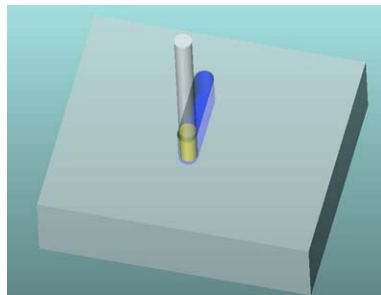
Exemple d'operació de ranuratge amb fresatge frontal
